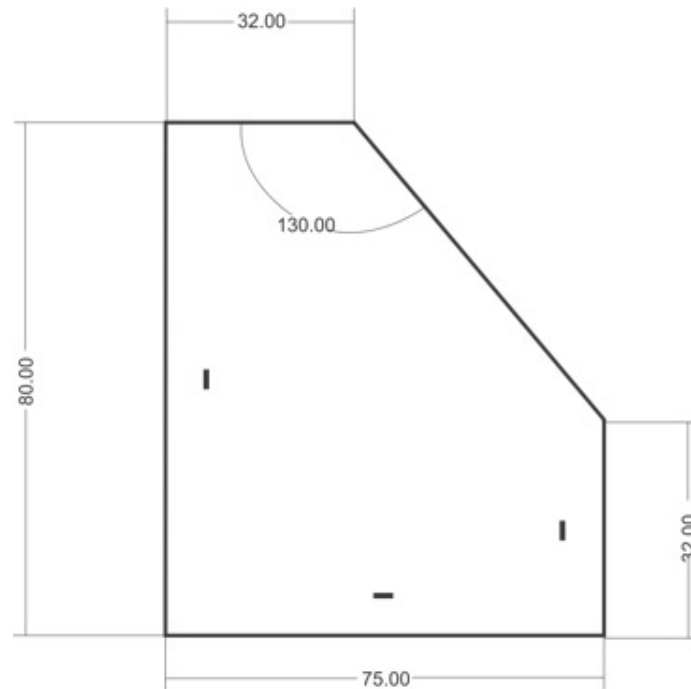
Pieza que se debe construir (Las medidas están en milímetros mm)
